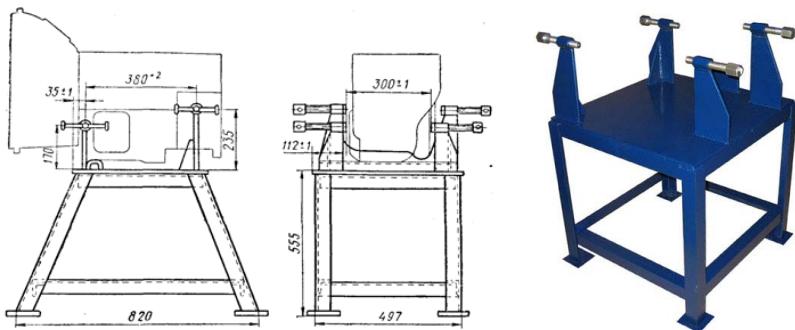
Стенд-верстак для закрепления агрегатов
